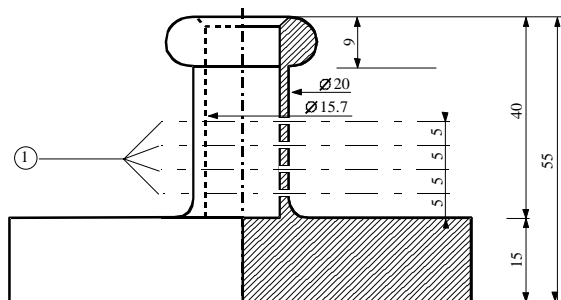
Cylindre creux en bronze, fermé d'un côté ; Plan et coupe verticale, dimensions en mm
